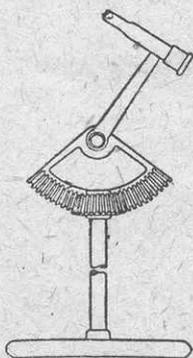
Ковническая шестерня и сегмент конической зубчатки рулевого управления (обратимый руль).
